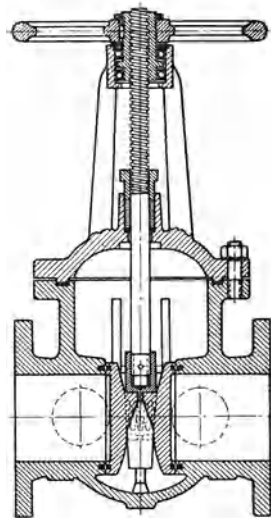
Parallelschieber dampfdichtend mit zusätzlicher mechanischer Plattenanpressung.
